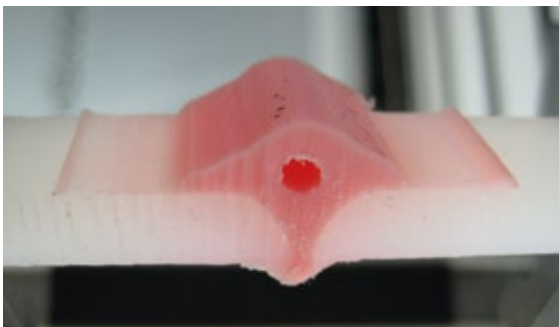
Zugprobe mit Vakuolen in der Schweißnaht
